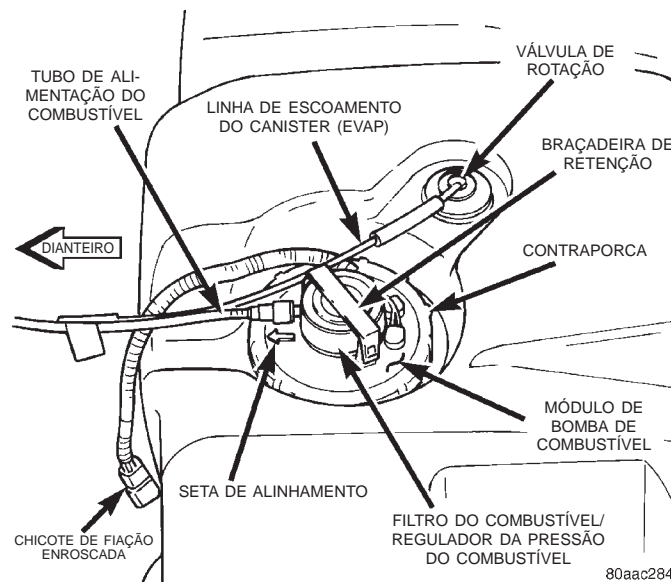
Reservatório de Combustível/Módulo de Bomba de Combustível (Vista Superior)
